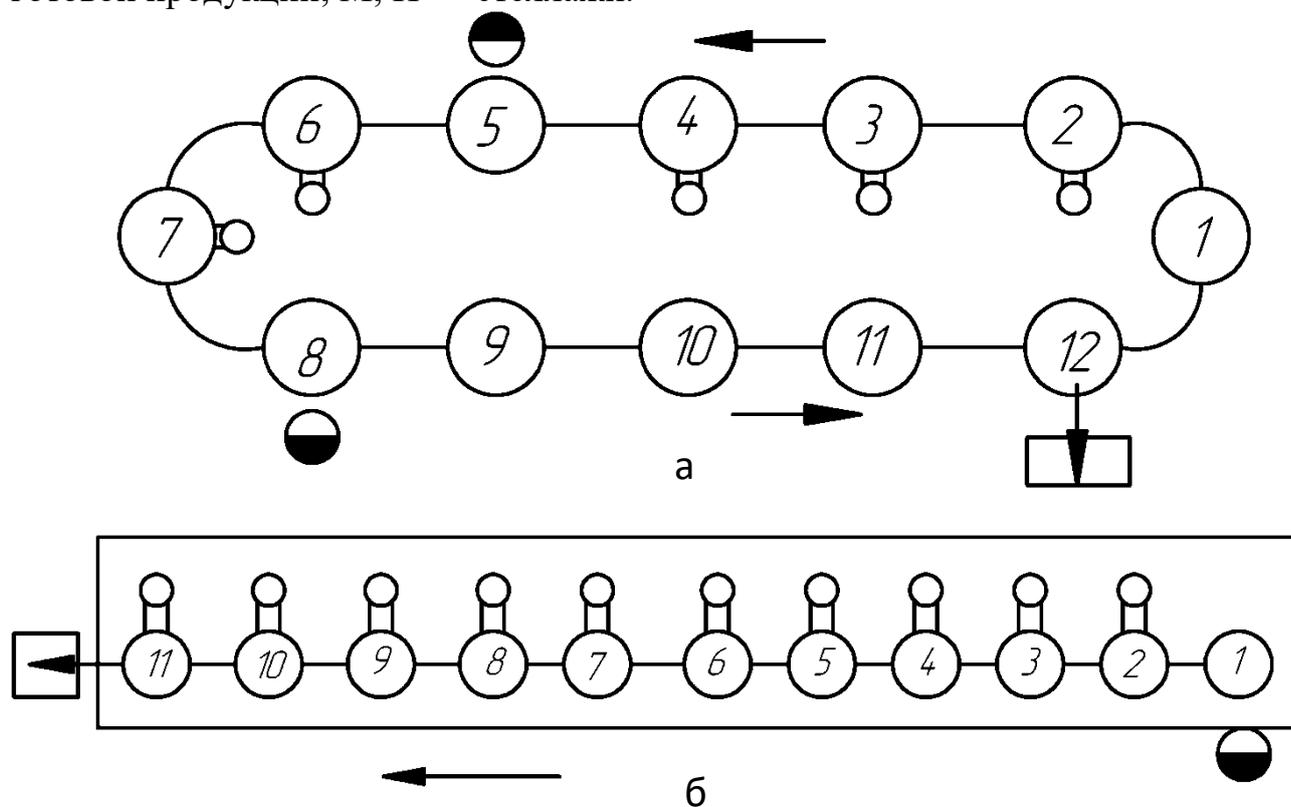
Схемы сборки узлов на автоматической или полуавтоматической линии: а – с замкнутым размещением сборочного оборудования (1 – позиция ручной загрузки; 2, 3, 4, 6, 7 – позиции автоматической сборки с автоматической подачей деталей из бункеров; 5, 8 – позиции ручной сборки; 9, 10, 11 – позиции продувки, контроля, смазки; 12 – позиция разгрузки собранного узла); б – с линейным размещением сборочного оборудования (1 – позиция ручной загрузки; 2 - 11 – позиции автоматической сборки узла)
